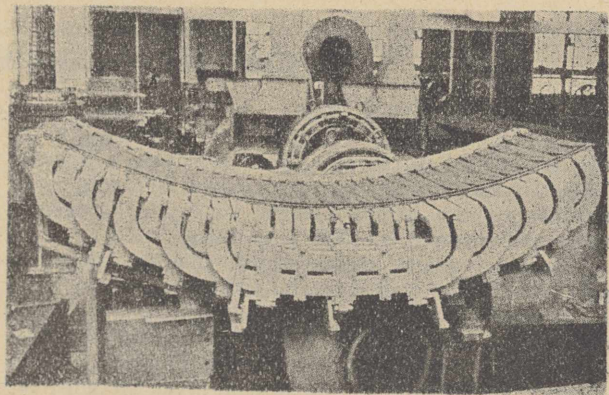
i 4 przedstawiają mieszadło indukcyjne, zamontowane w 10 t piecu w Surahammar.
